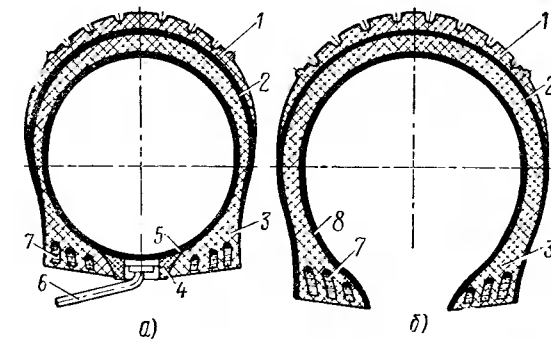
Конструкция камерного (а) и бескамерного пневматиков (б):
